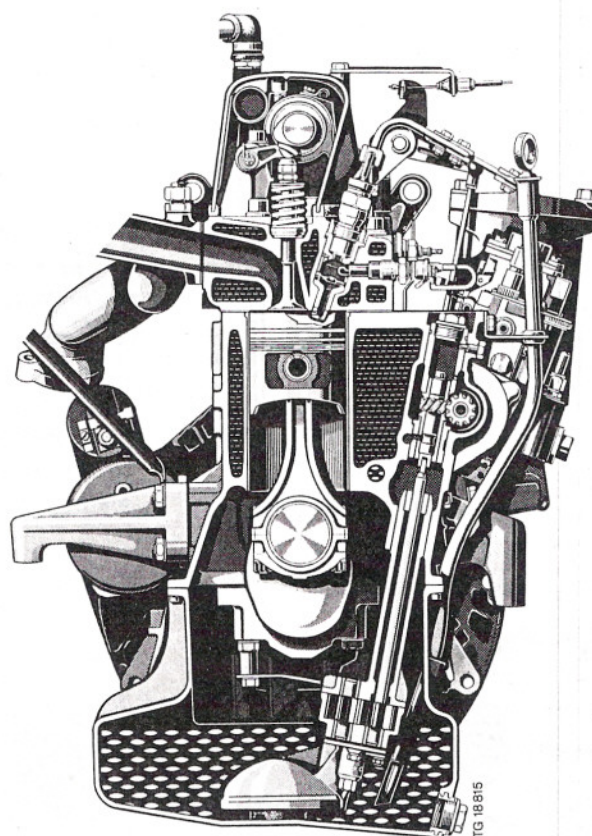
Motor Diesel 616 (Ejec. 616.936) – sección transversal
